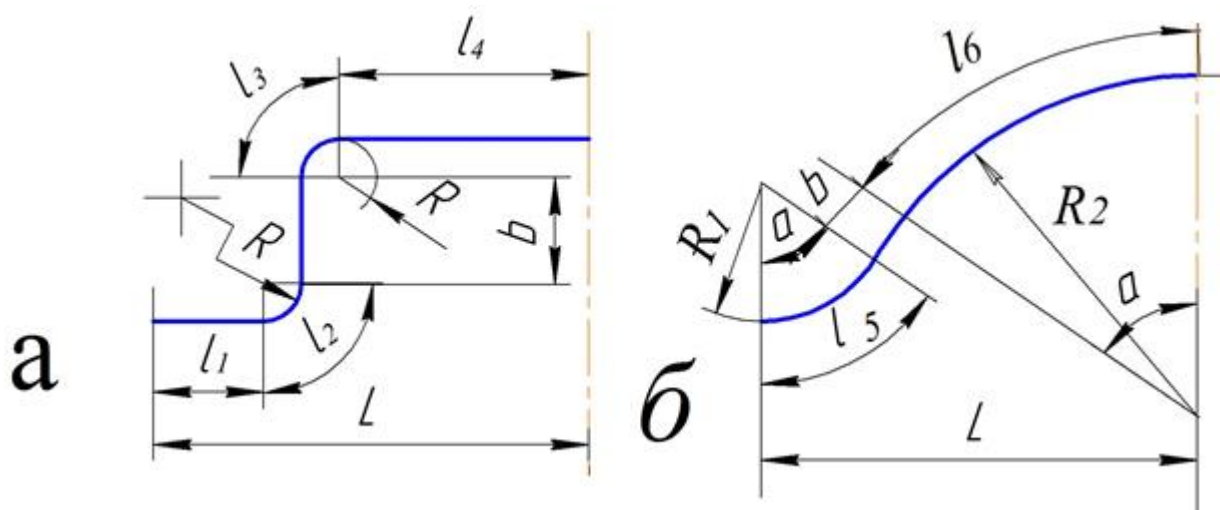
Схема для визначення параметрів хвилястої заготовки з похилою прямолінійною ділянкою: а – гофрований профіль; б – хвиляста заготовка
